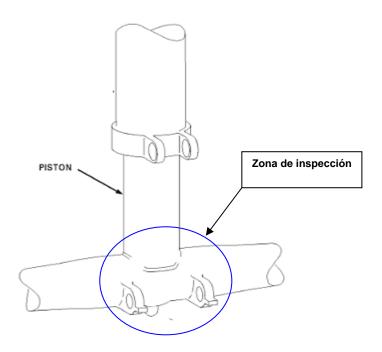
Se ilustra la zona de inspección del pistón en el tren de aterrizaje principal.
